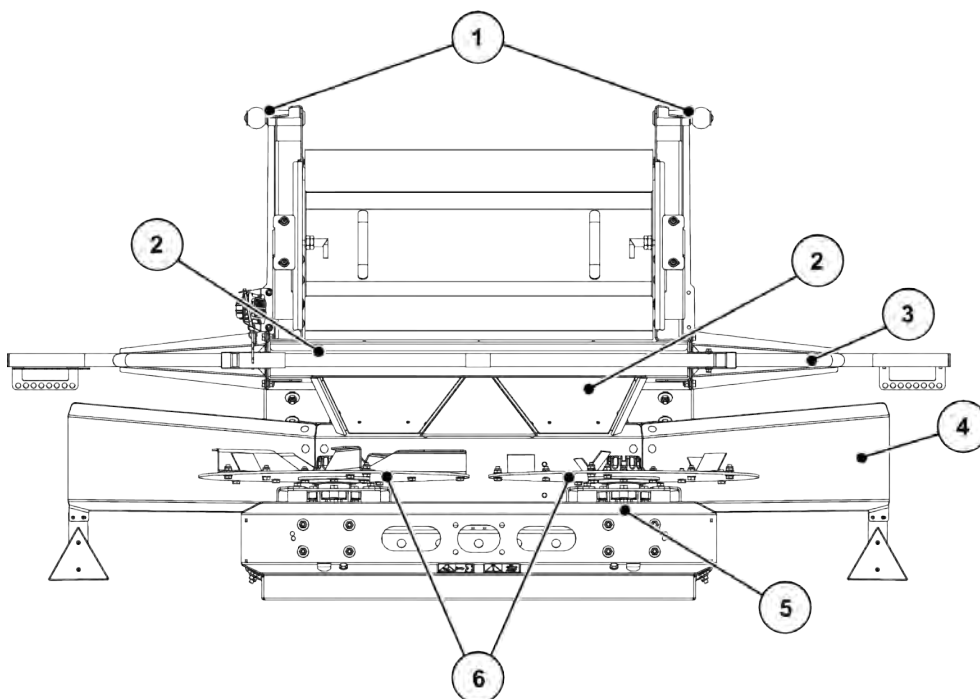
Baugruppenübersicht des Universaltreuwerks UNIVERSAL-PowerPack
